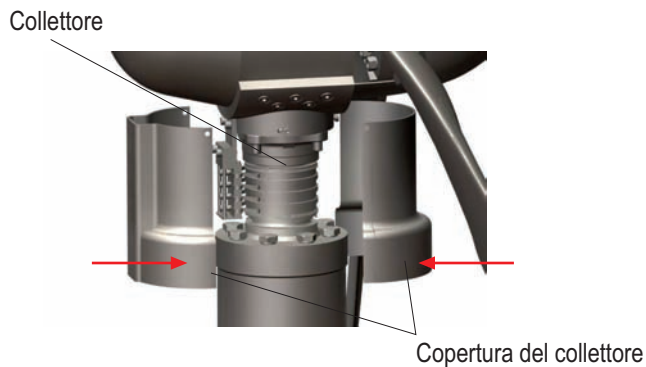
Dettaglio montaggio dell'involucro del collettore.
